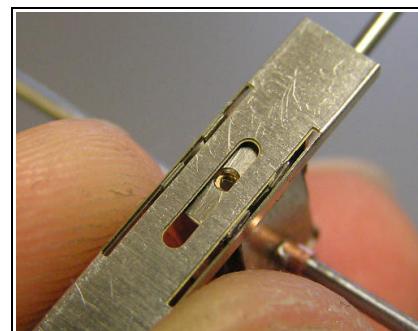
Die Achse soll so in dem Chassisblech passen. Die Position ist in der Länge (Achsabstand) einstellbar.
